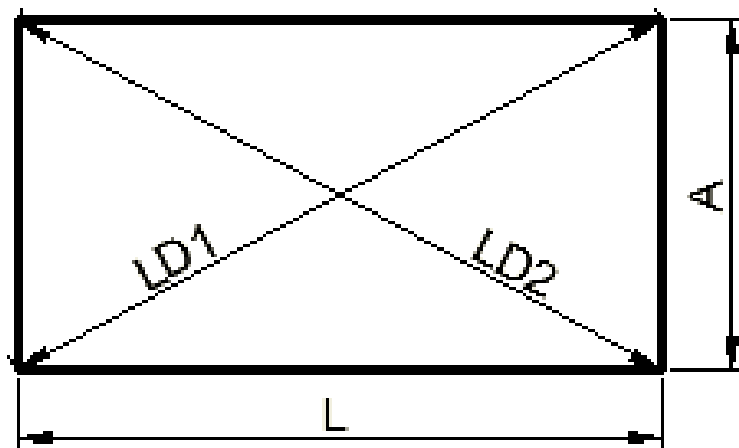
PARÁMETROS DE CONTROL DIMENSIONAL (6)
